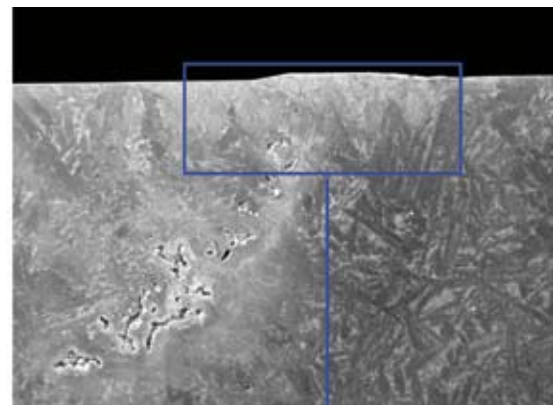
Querschliff einer manuellen Laserstrahlschweißung mit Porosität im Grundwerkstoff
